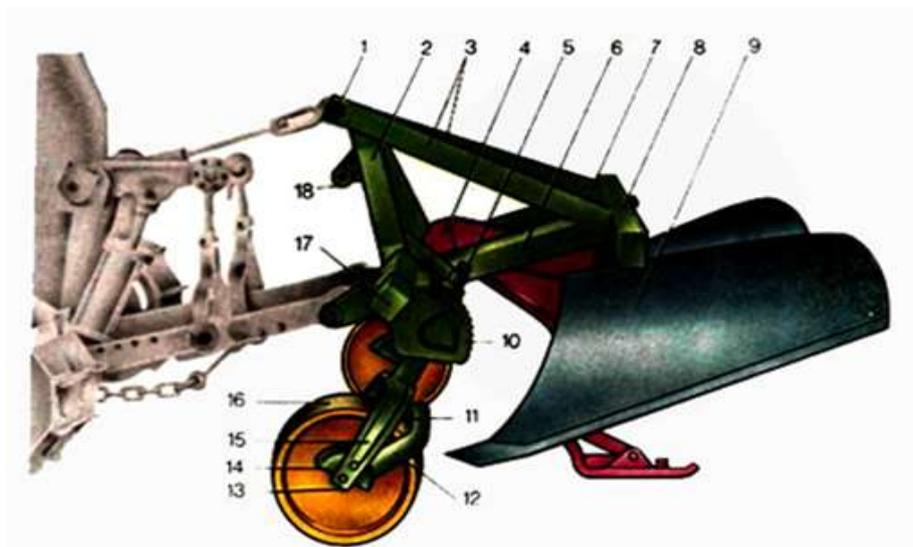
Канавокопатель-заравниватель универсальный КЗУ-О.ЗВ:
